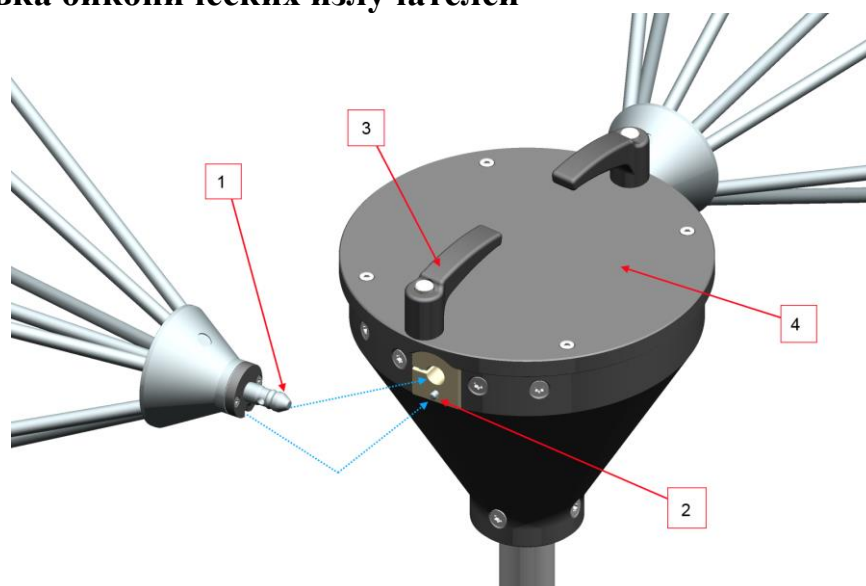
Установка вибраторов: 1) контактный болт, 2) фиксирующий штырь, 3) фиксирующая рукоятка, 4) корпус.
